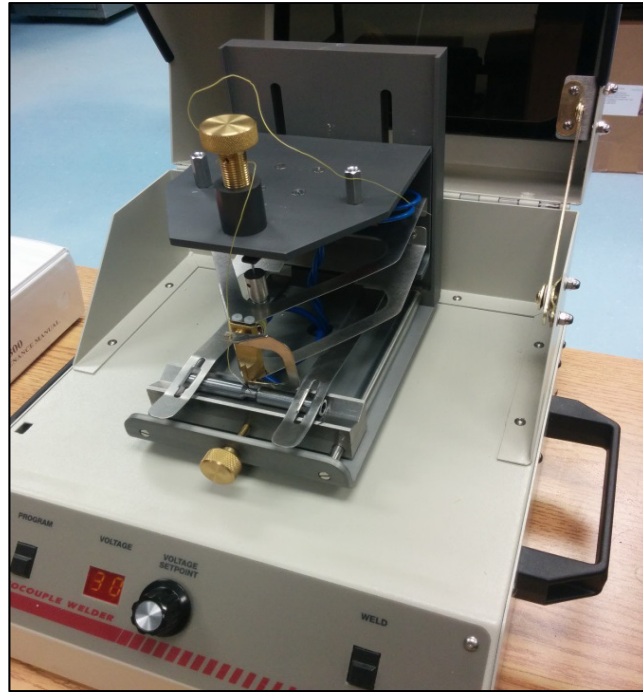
Thermocouple Welder permettant de souder les thermocouples sur l'éprouvette
